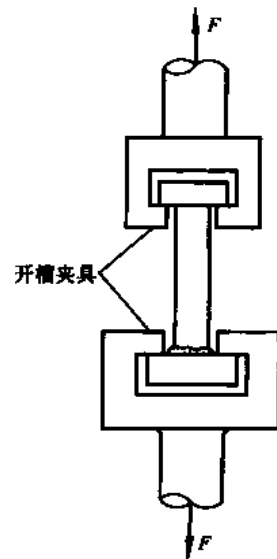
螺柱焊接头拉伸试验用夹具形式
